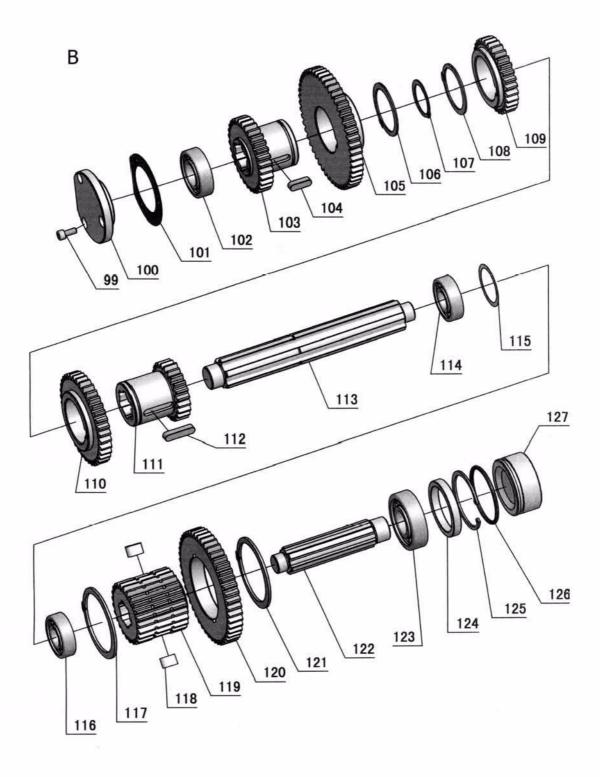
Spindelstock 4 von 8 - Headstock 4 of 8
